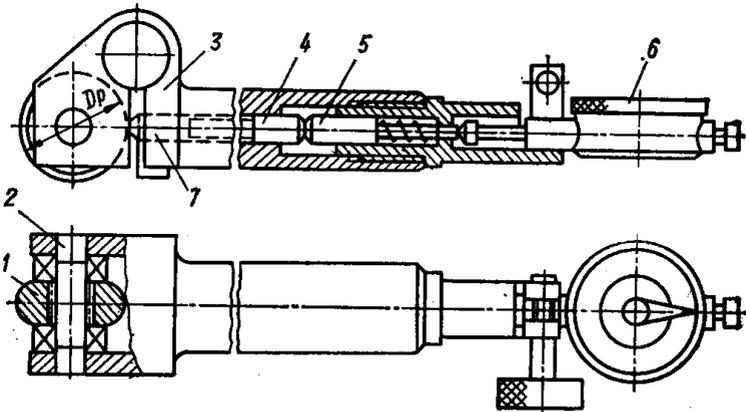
Інструмент для обкатування зовнішніх циліндричних поверхонь:
